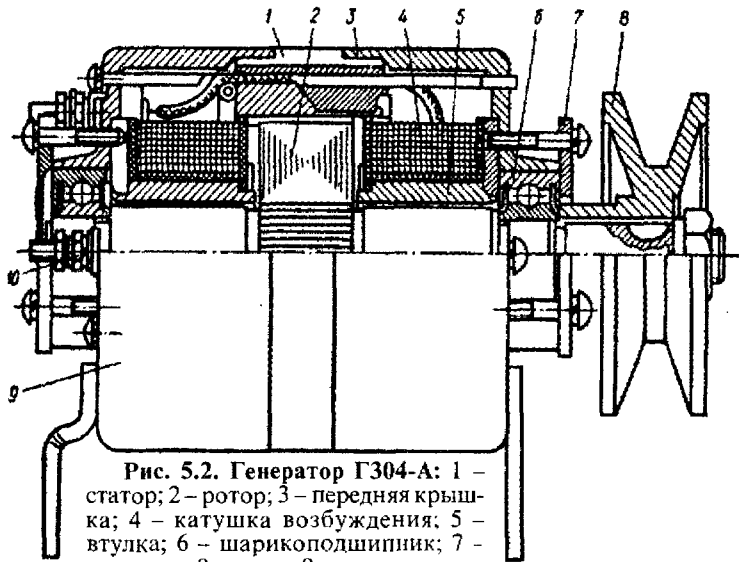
Генератор Г304-А: 1 - статор; 2 - ротор; 3 - передняя крышка; 4 - катушка возбуждения; 5 - втулка; 6 - шарикоподшипник; 7 - пластина; 8 - шкив; 9 - задняя крышка; 10 - вывод фазы
